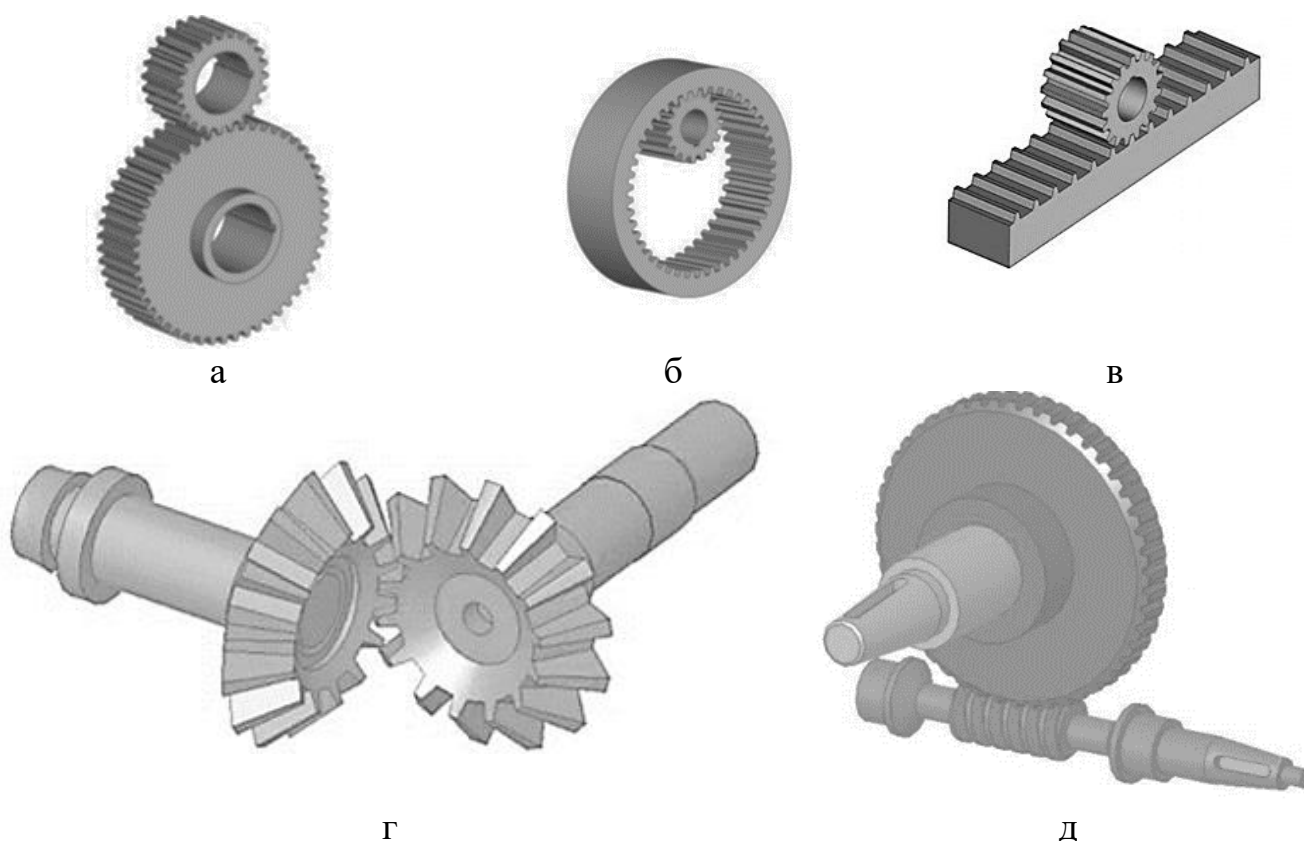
Виды зубчатых передач: а — цилиндрическая зубчатая передача с внешним зацеплением; б — цилиндрическая передача с внутренним зацеплением; в — реечная передача; г — коническая зубчатая передача; д — зубчатая винтовая передача.
